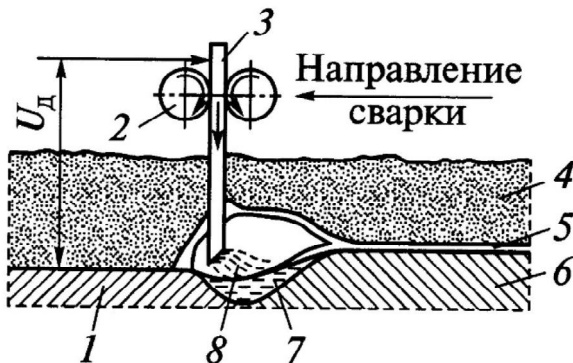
Схема флюсовой защиты металла при сварке:
